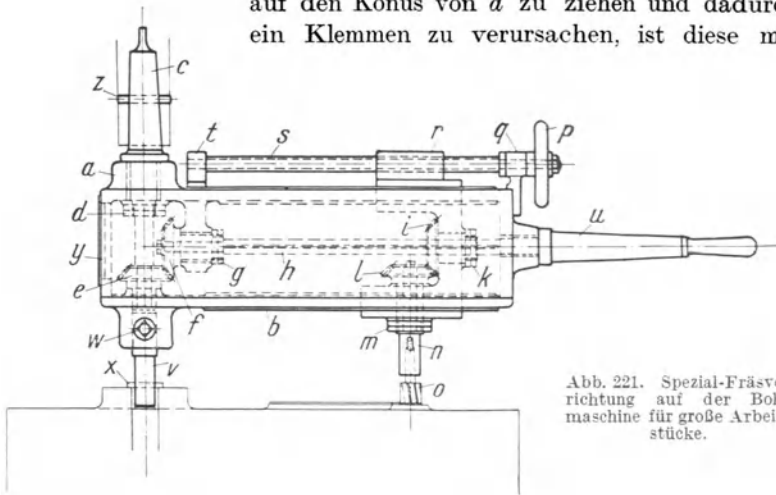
Spezial-Fräsvorrichtung auf der Bohrmaschine für große Arbeitsstücke.
